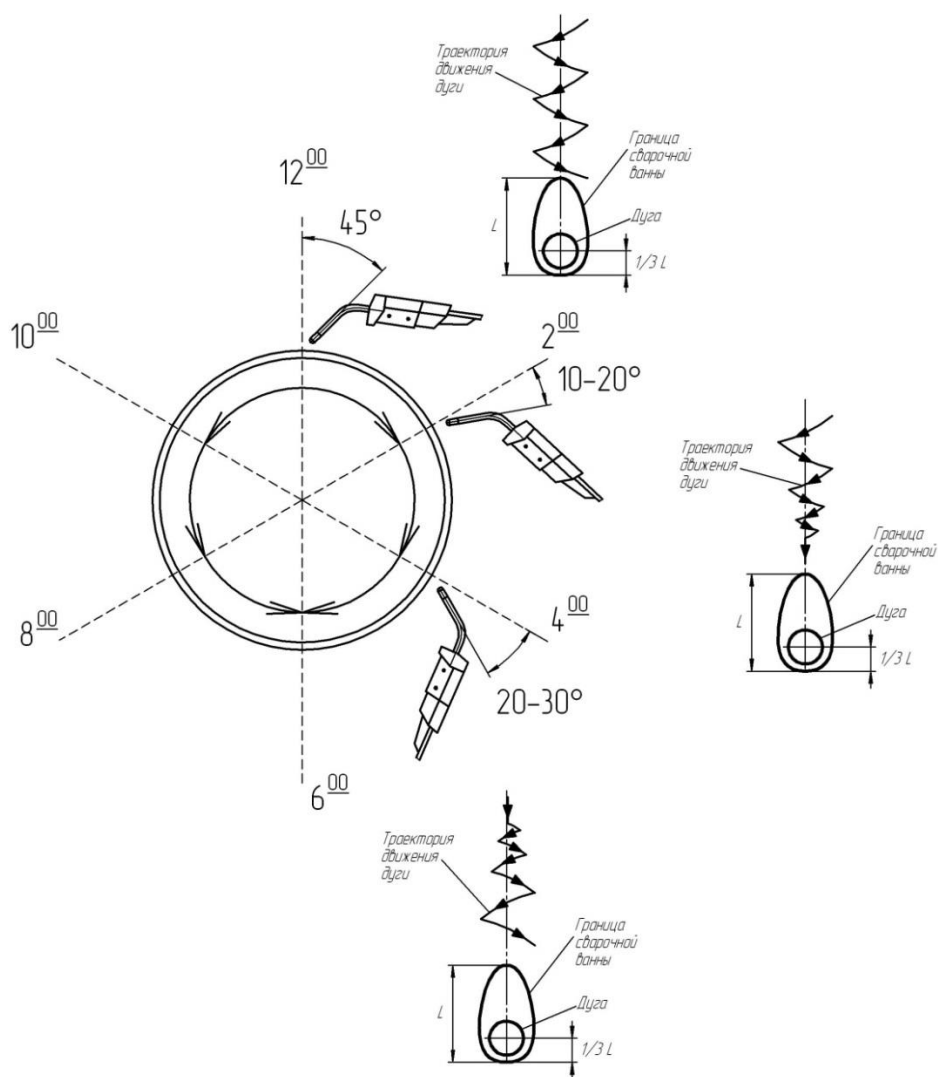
Техника сварки стыка труб по технологии STT
